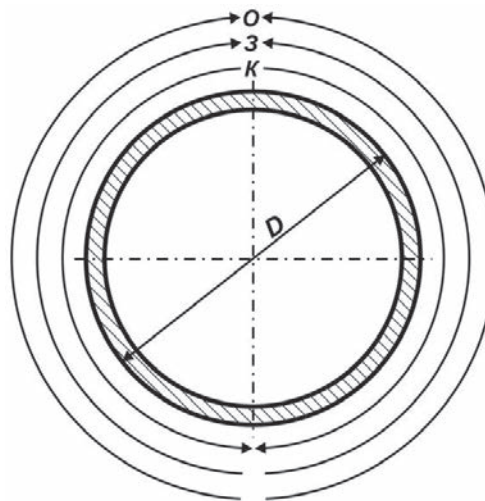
Направление сварки кольцевого стыкового соединения: К – корневой; З – заполняющий; О – облицовочный проходы
